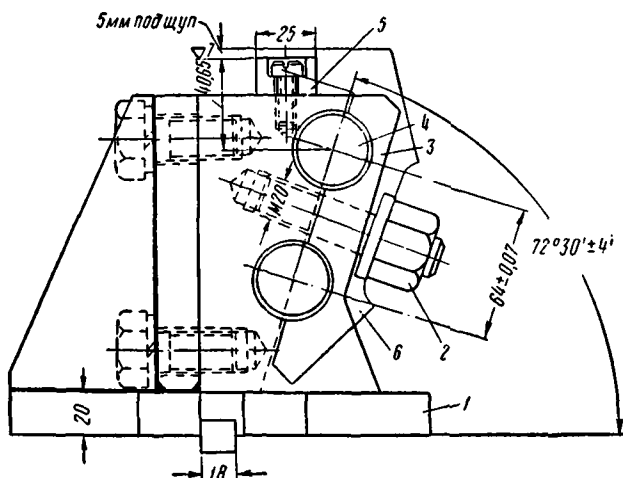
Приспособление для фрезерования гребенки и сверления отверстия в корпусе кронштейна двигателя НБ-412М:
